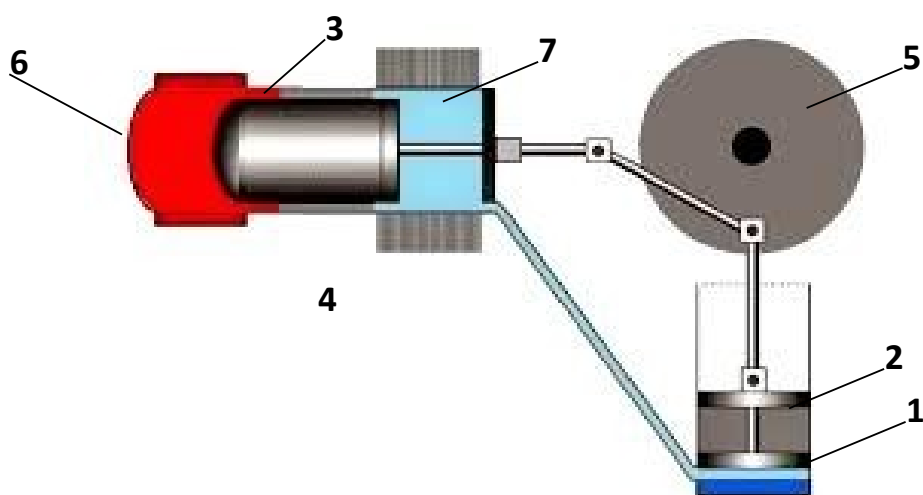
Конструкция двигателя Стирлинга типа «Гамма»
